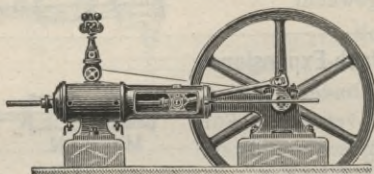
Maschinen mit Bajonettrahmen bis 800 Hub und hinten geführter Kolbenstange.
